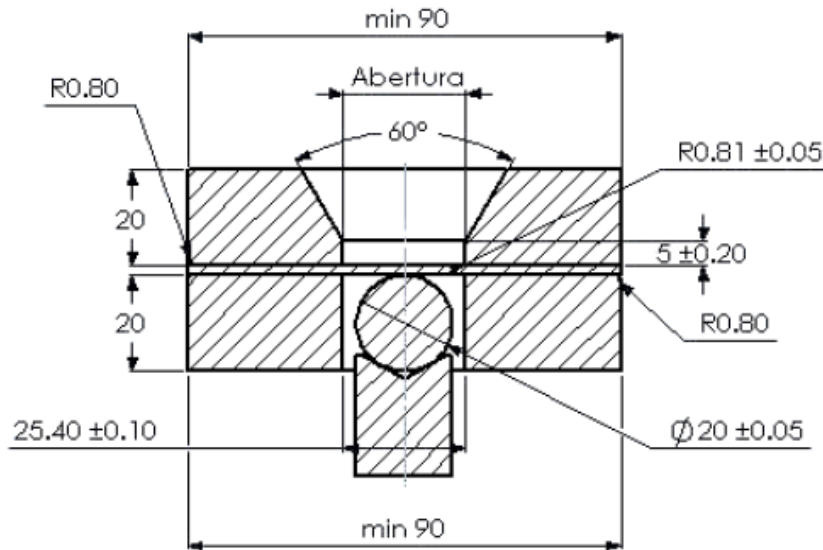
Dimensiones estándar ASTM E643 en milímetros [6].
